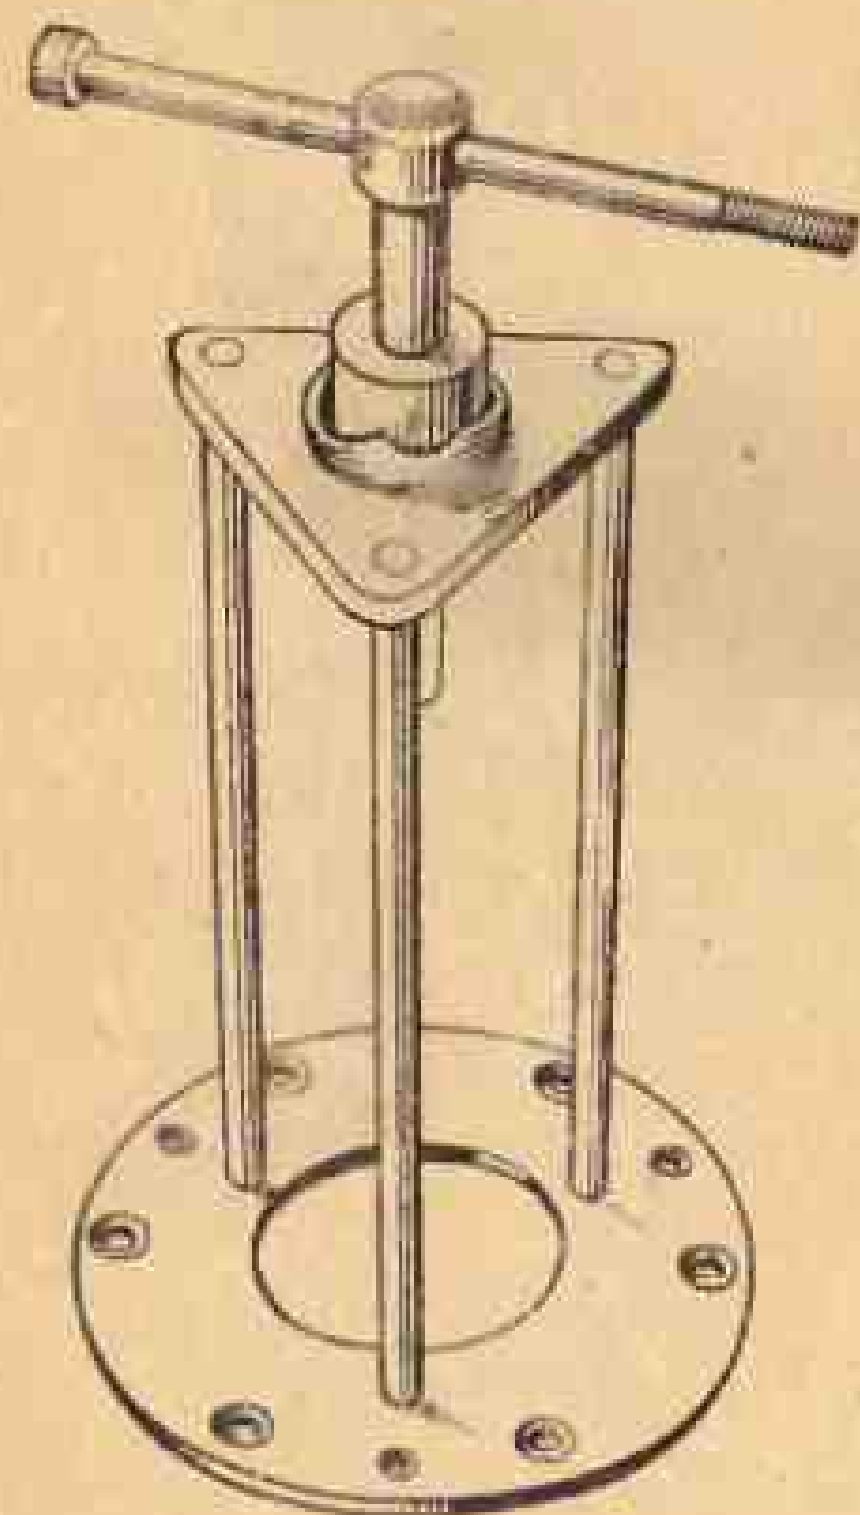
Съёмник для основной части картера с упорной шайбой новой конструкции
